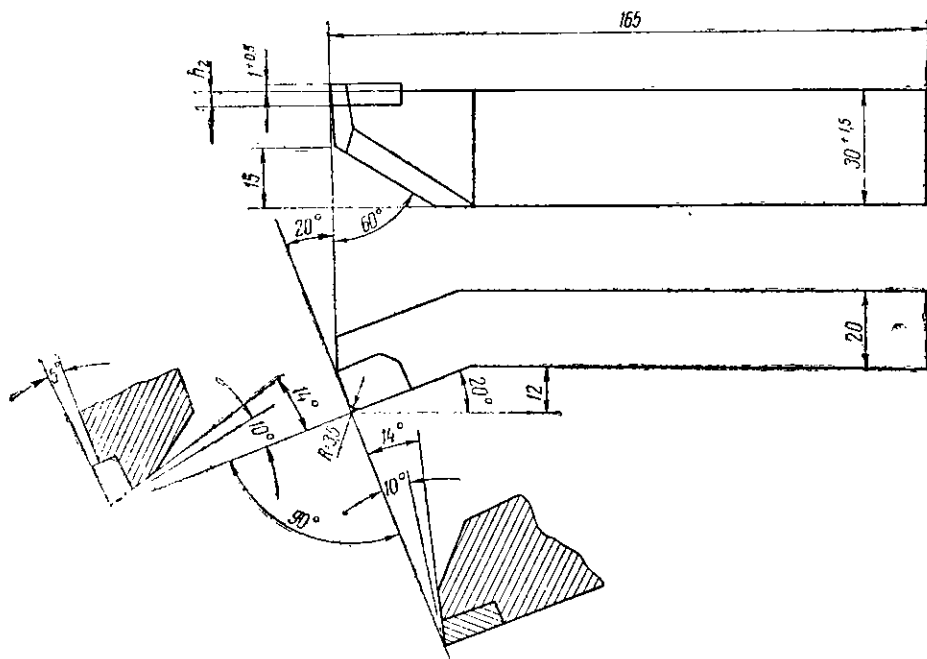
Проходной резец для обточки подшлипниковых колец на станках МР5 (завод им. Куйбышева).
